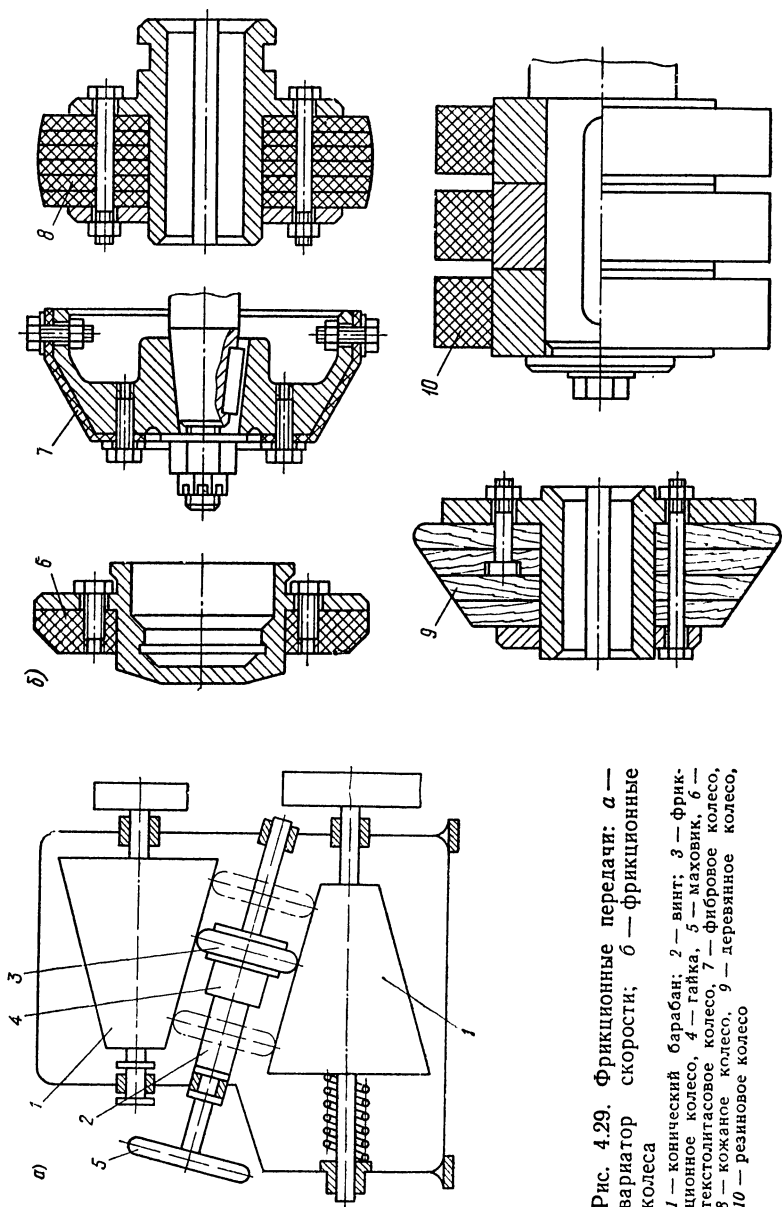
Фрикционные передачи: а — вариатор скорости; б — фрикционные колеса
